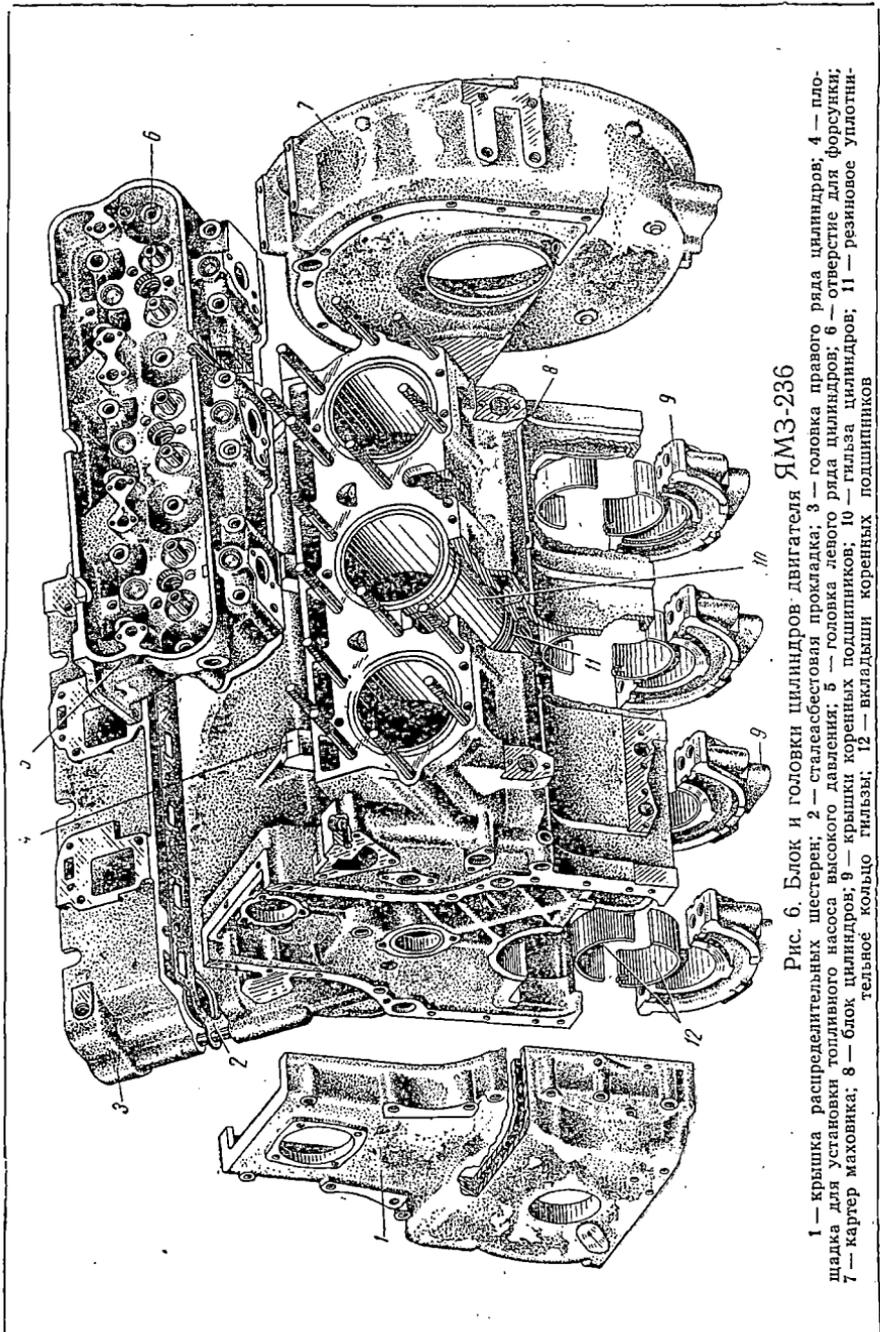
Блок и головки цилиндров двигателя ЯМЗ-236
